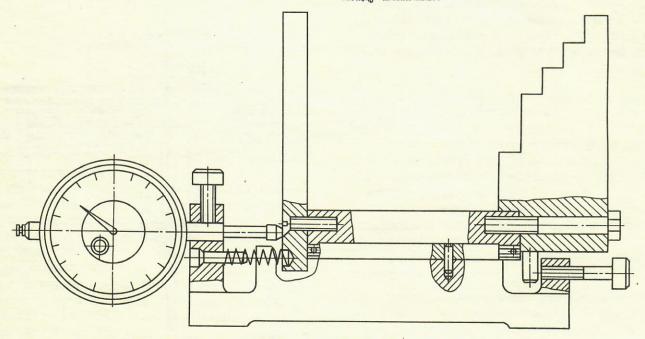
Приспособление для установки резца на шпинделе 🛭 78 мм
